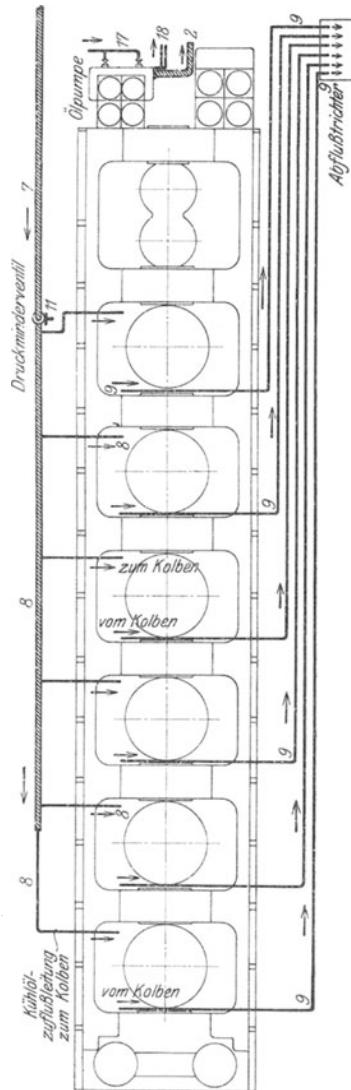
Schema der Schmieröl- und Ölkühlleitungen einer Tauchkolbenmaschine.
